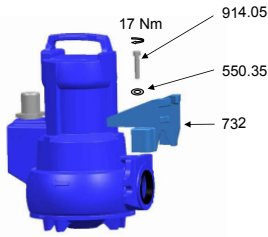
Montaje del soporte con guía del cable, guía de bielas simple y guía de estribo
